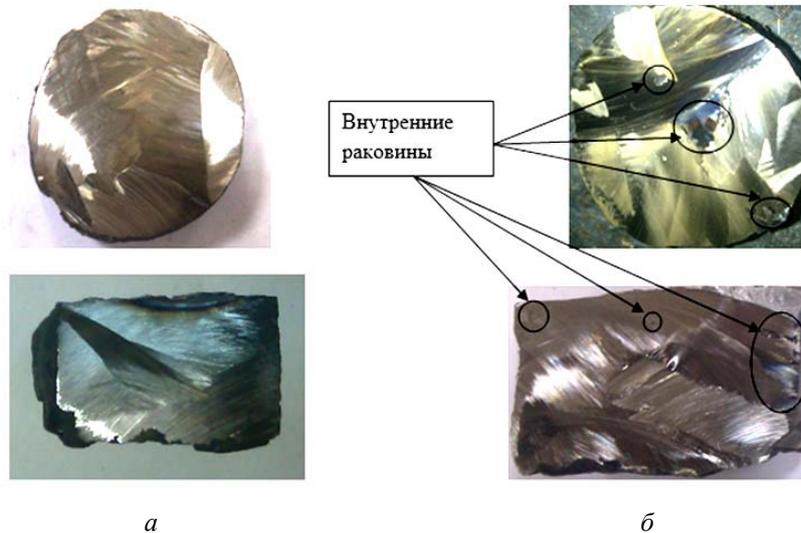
Образцы, вырезанные из отливок стали 35ГЛ:
